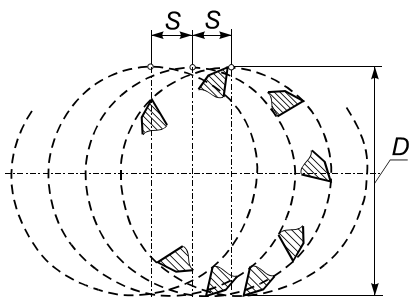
Траектория рабочего движения точки лезвия цилиндрической фрезы
